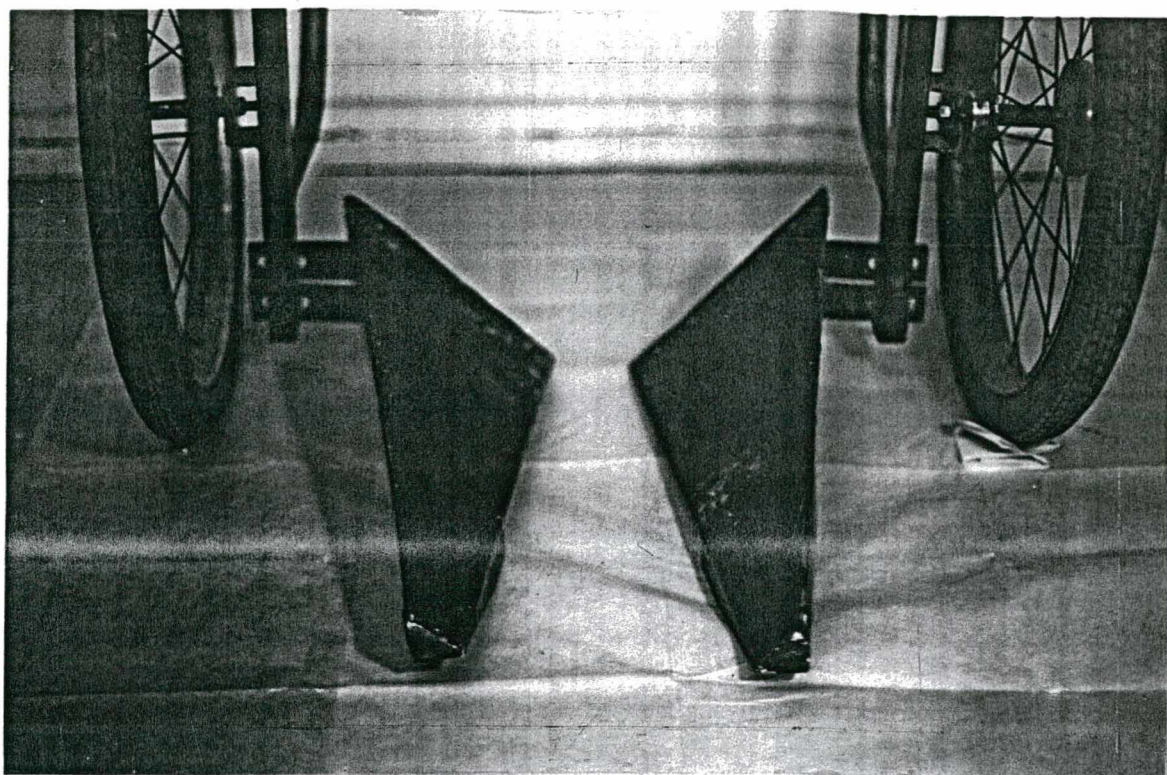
c: Levantador com 3 faces e face interna a 45° .
